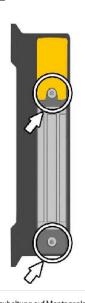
Prozesszuhaltung auf Montageplatte anbringen und Schrauben M6 x 25 mm Torx festziehen.
